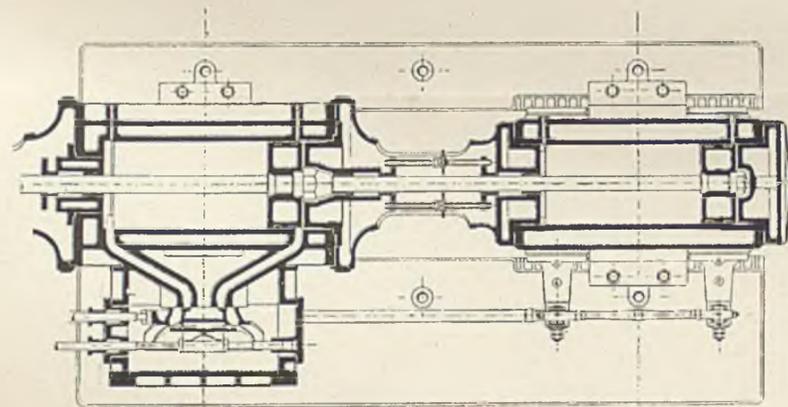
Schnitt durch die Hochdruckeylinder des liegenden Stufen Kompressors von Th. Calow & Co., Bielefeld.
